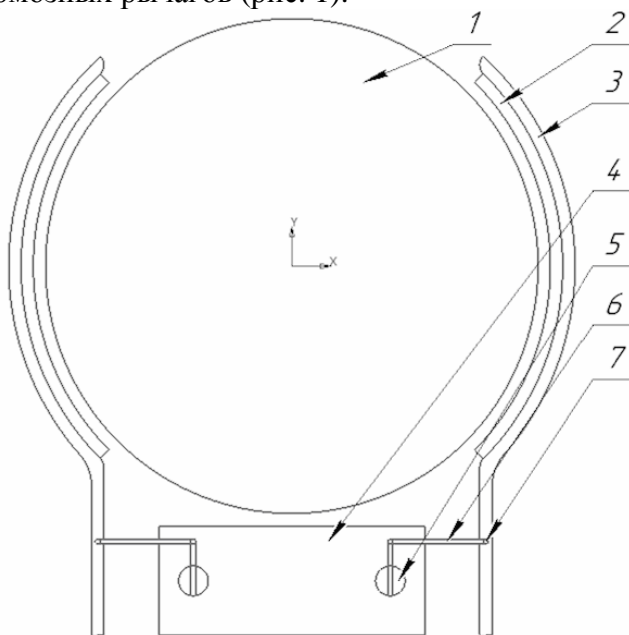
Схема устройства контроля положения тормозных рычагов: 1 – тормозной барабан; 2 – тормозная накладка; 3 – тормозной рычаг; 4 – кронштейн; 5 – переменный резистор; 6 – тяга; 7 – шарнир
